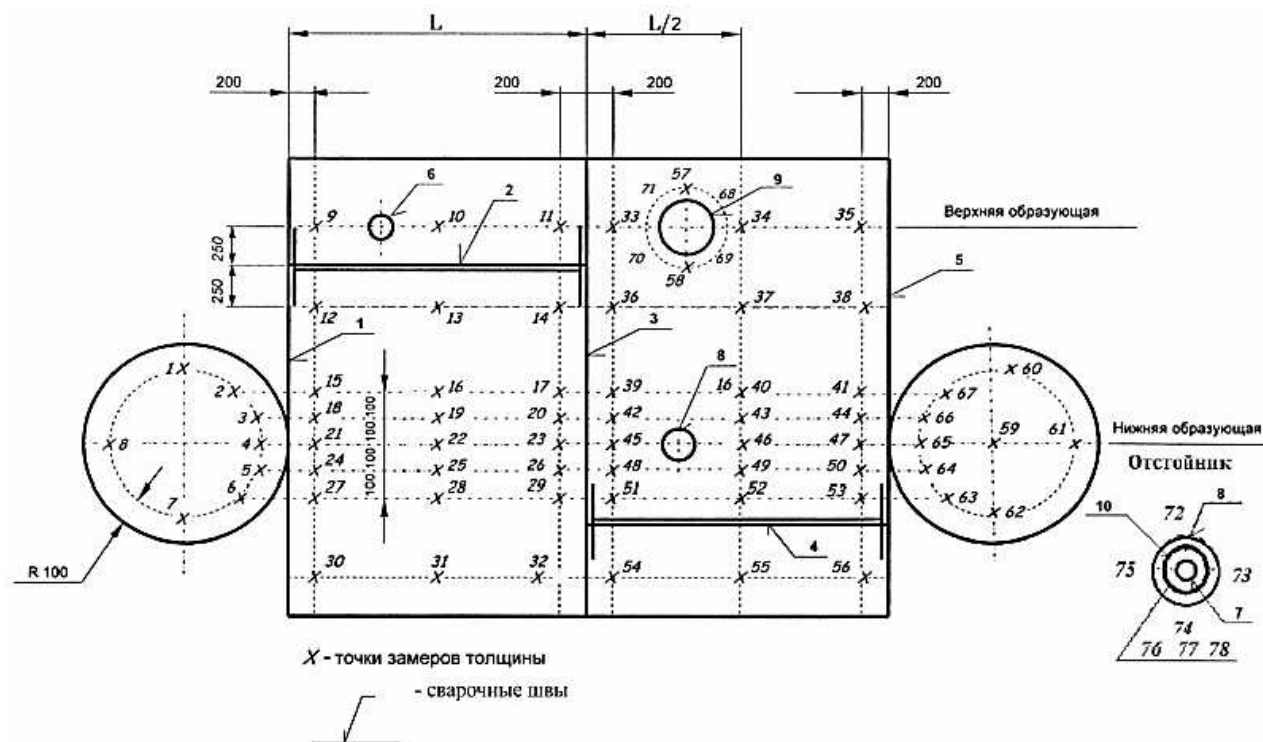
Резервуар установки использования сжиженных газов в развертке с указанием точек замера толщины и сварочных швов, подлежащих контролю
